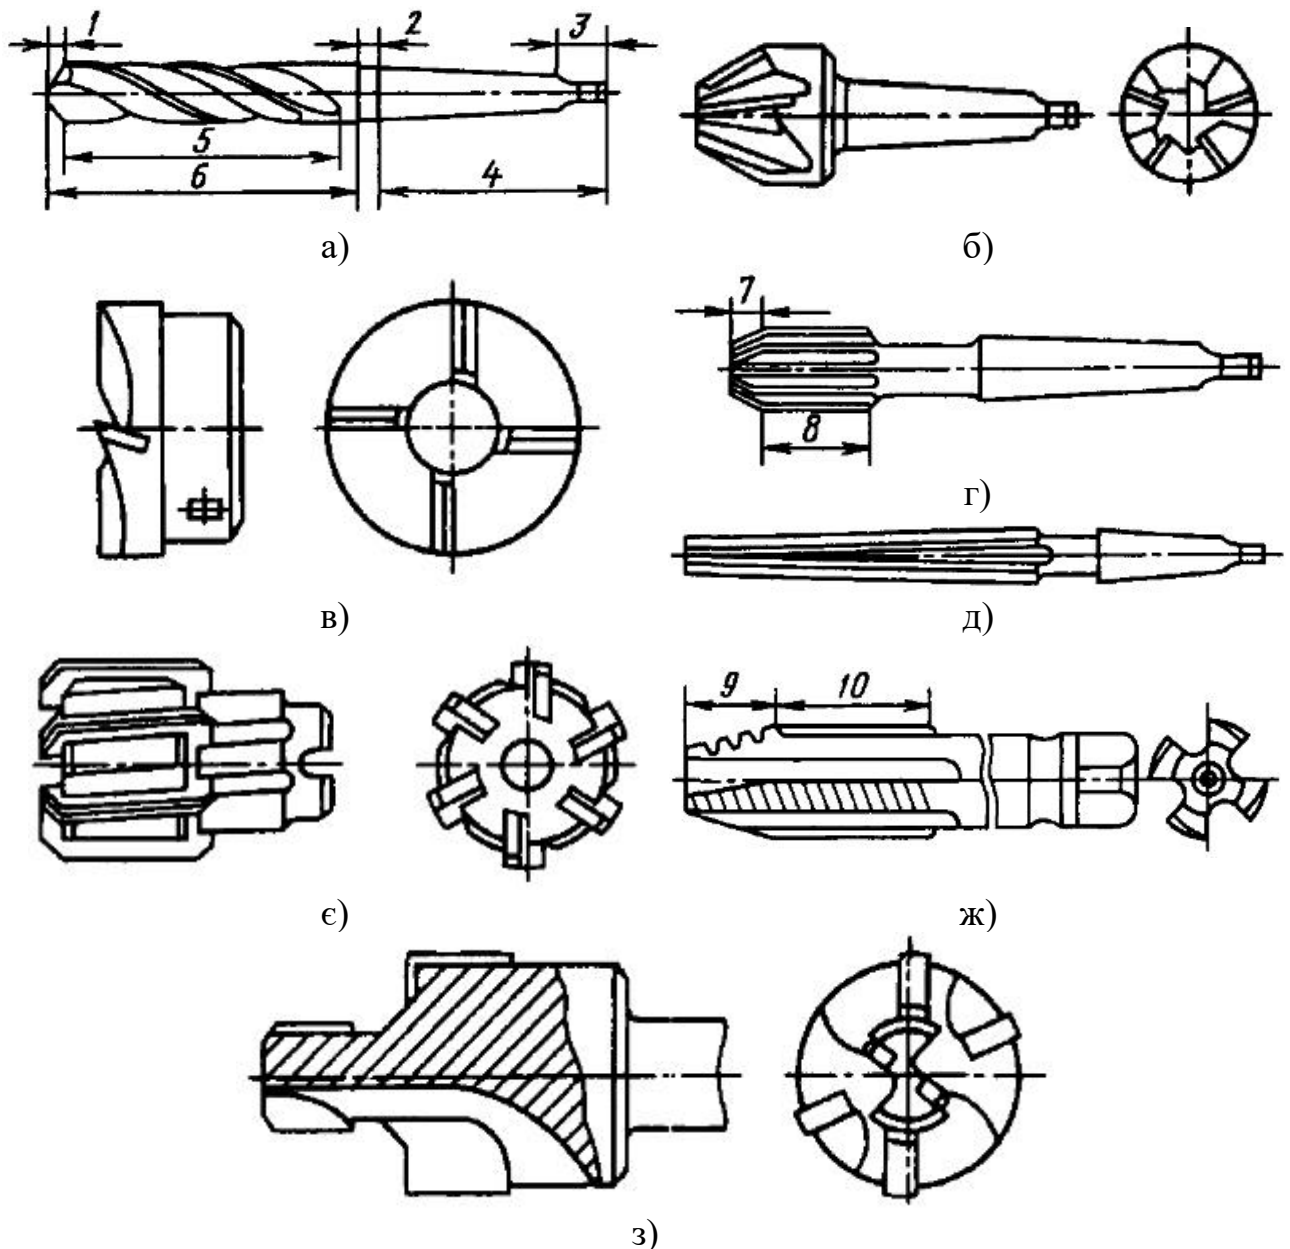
Інструменти для обробки на свердлильних верстатах:
